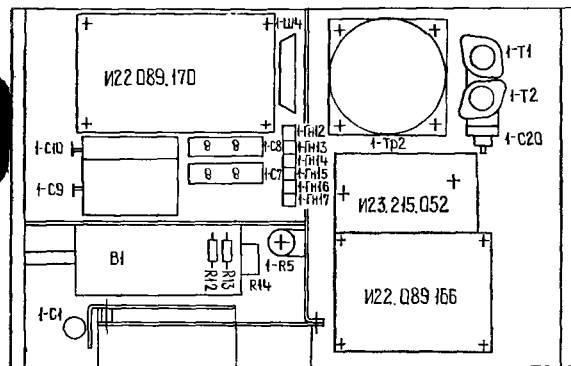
Схема расположения установочных элементов и печатных плат (вид снизу).
